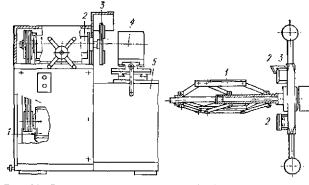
Станок для мехаиической обработки пластмассовых труб:
